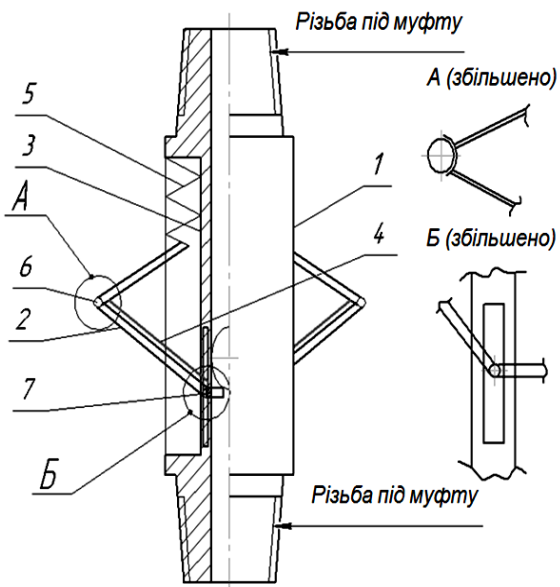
Схема пристрою для обробки стовбура свердловини
